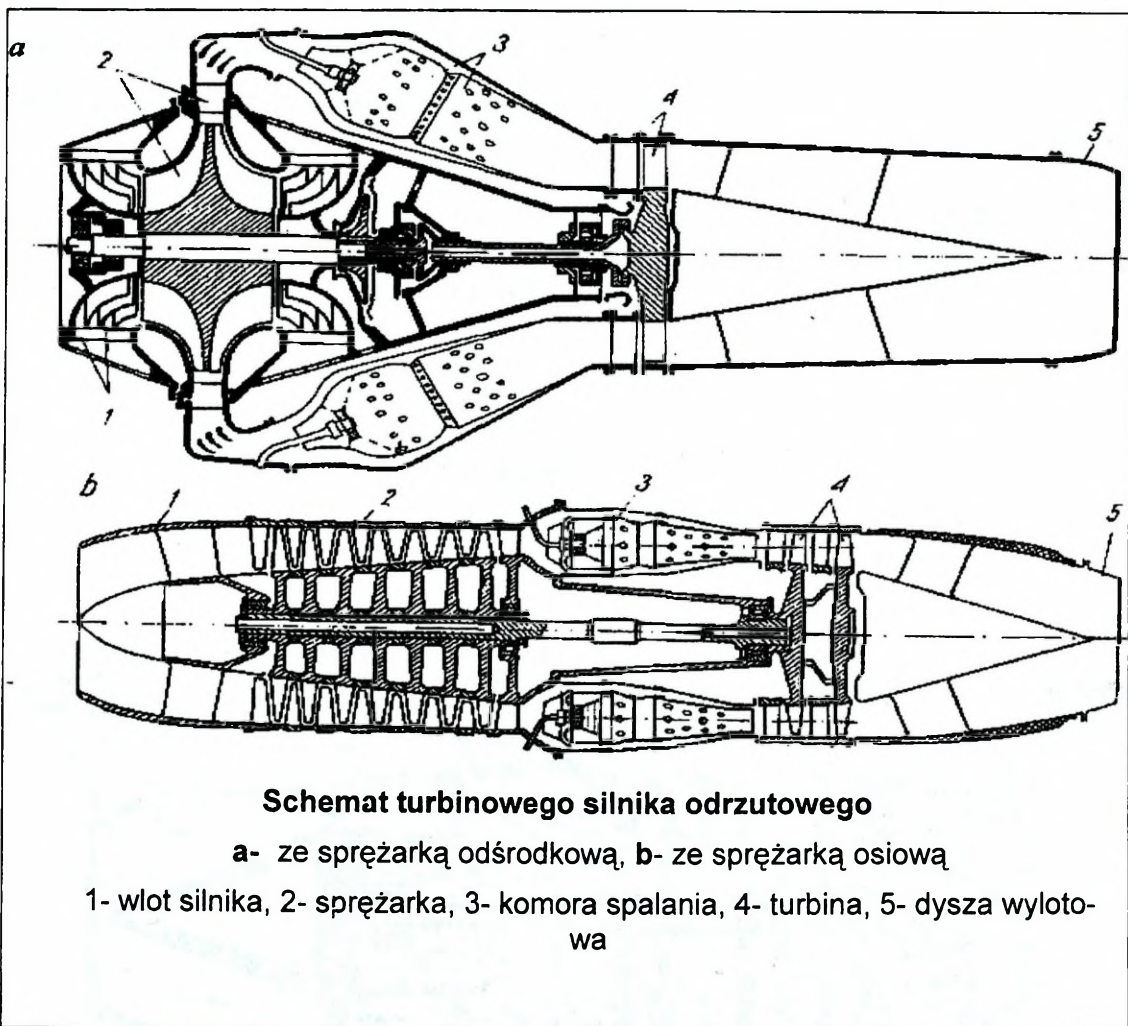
Przykłady rozwiązań konstrukcyjnych silników strumieniowych
